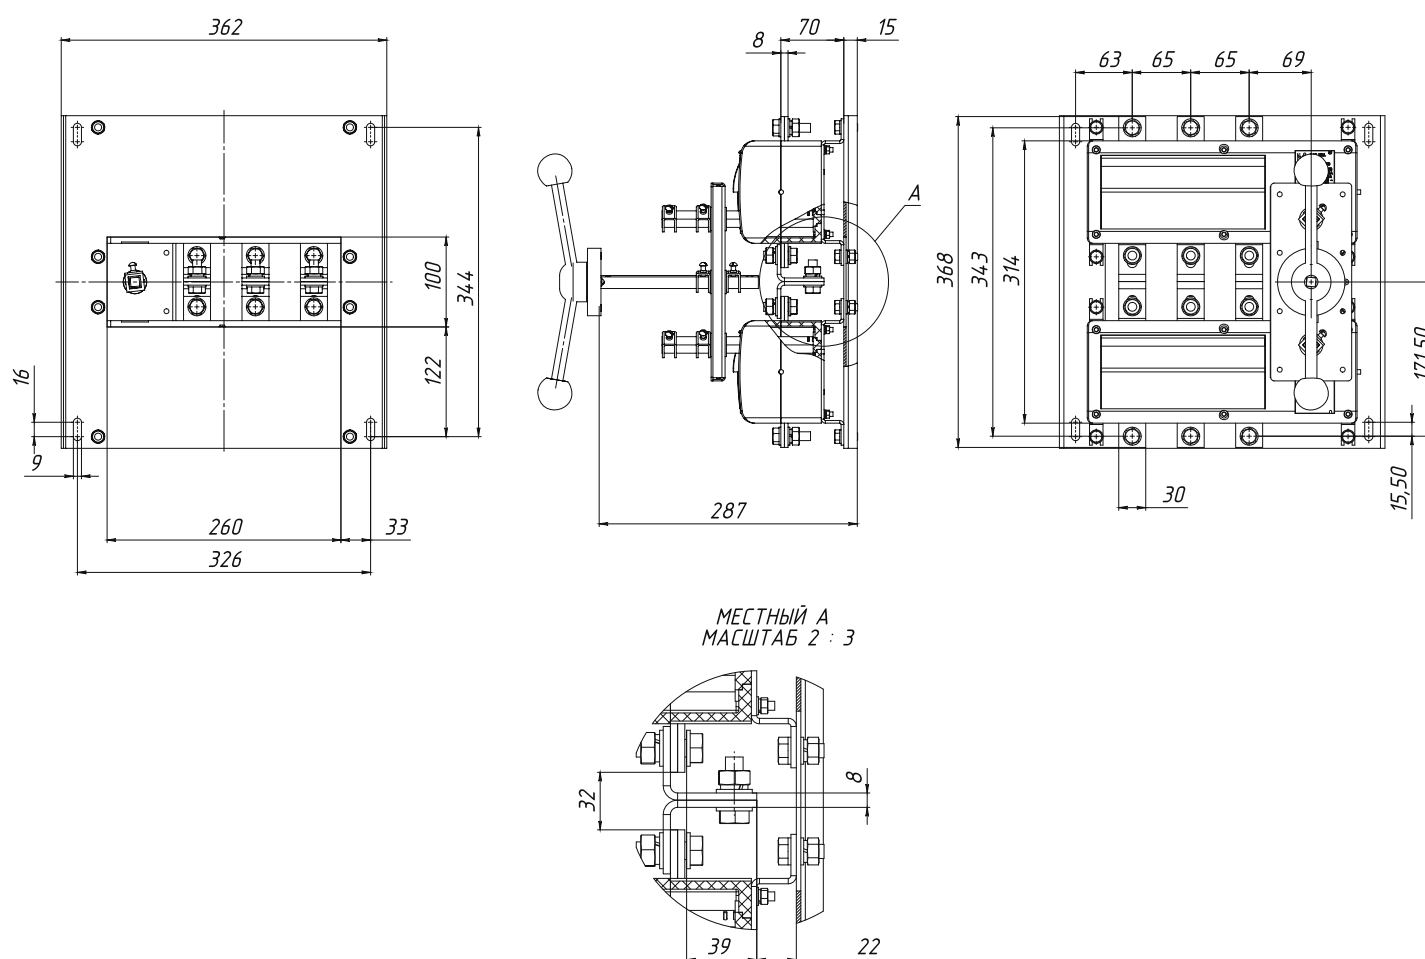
Выключатель-разъединитель ВНК-37-71130-32 УХЛ3
